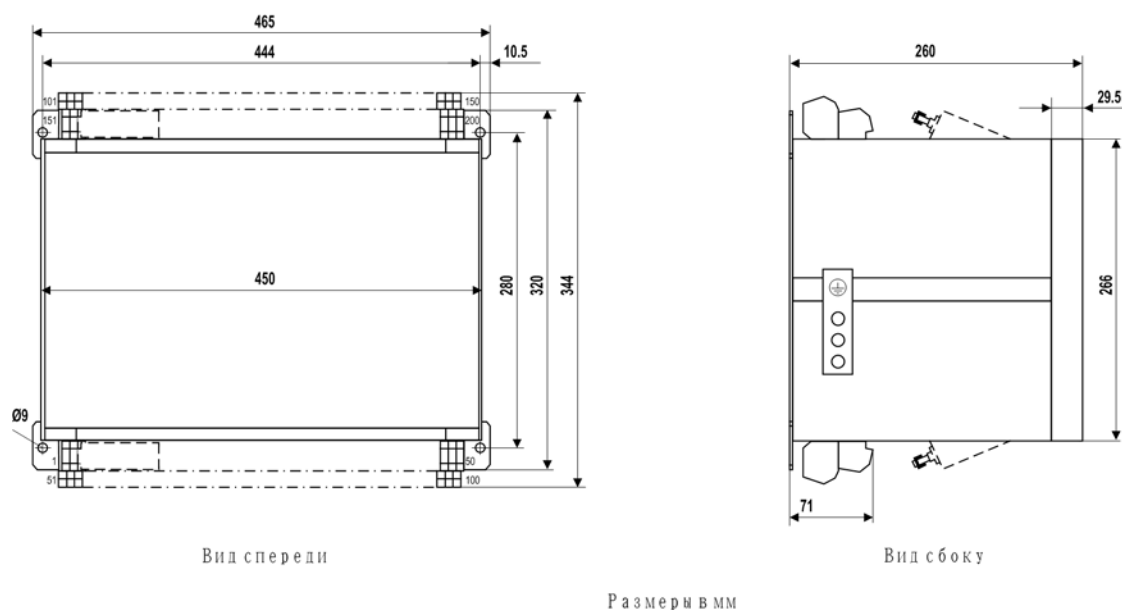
Размеры терминала 7UT633 или 7UT635 в корпусе для навесного монтажа (размер корпуса 1/1)
